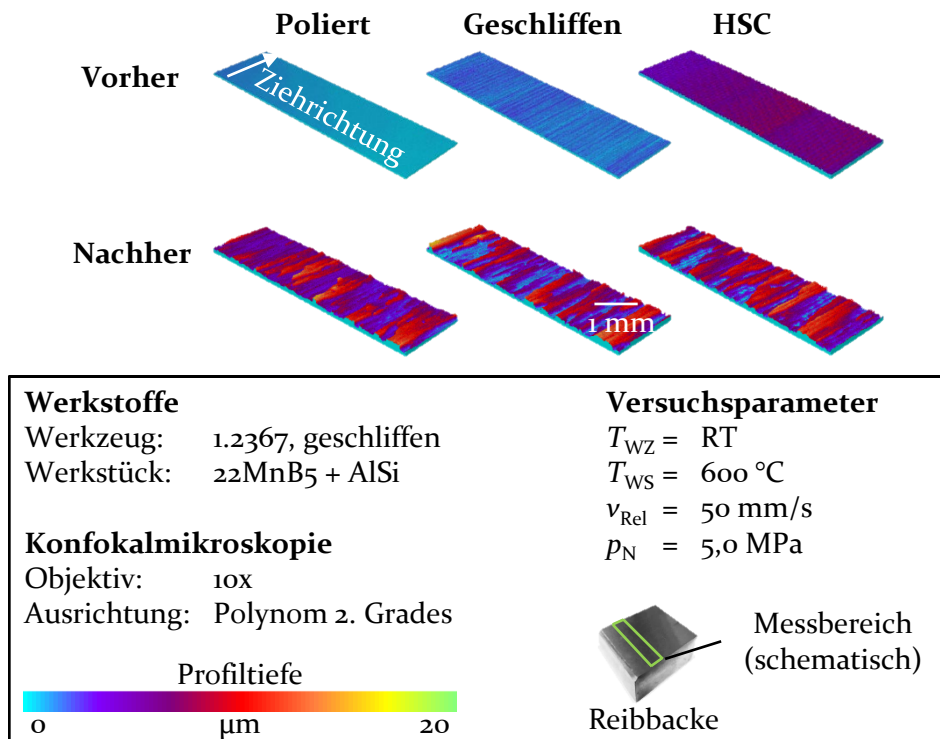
Topographiaufnahmen der Werkzeugoberfläche für unterschiedliche Oberflächenbearbeitung
